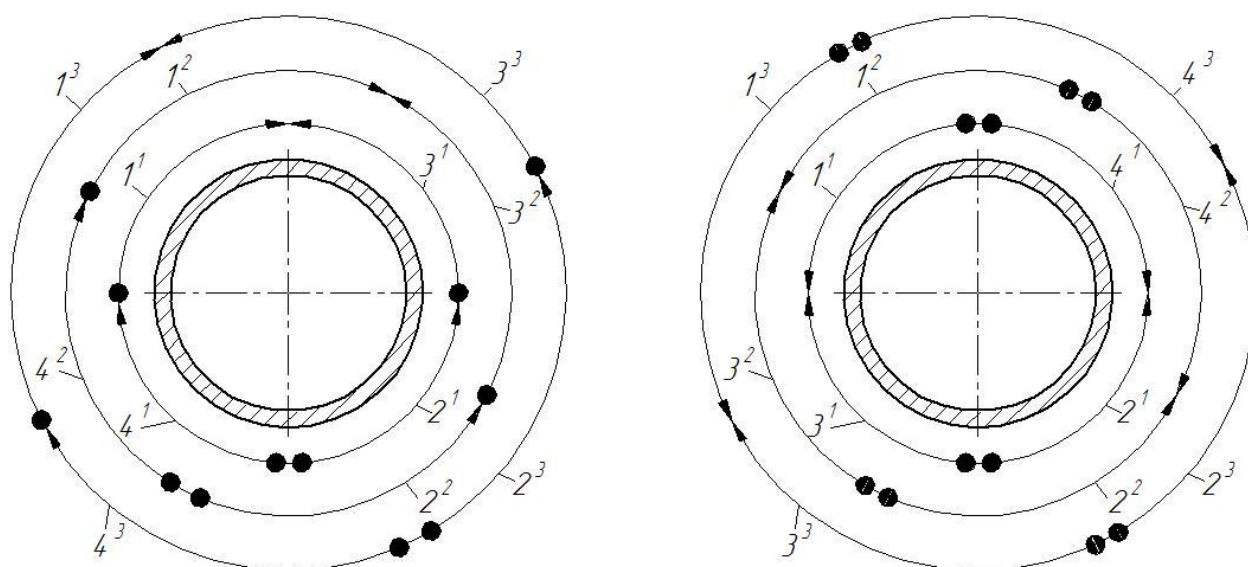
Порядок сварки слоёв при вертикальном (а) и горизонтальном (б) положении стыка
